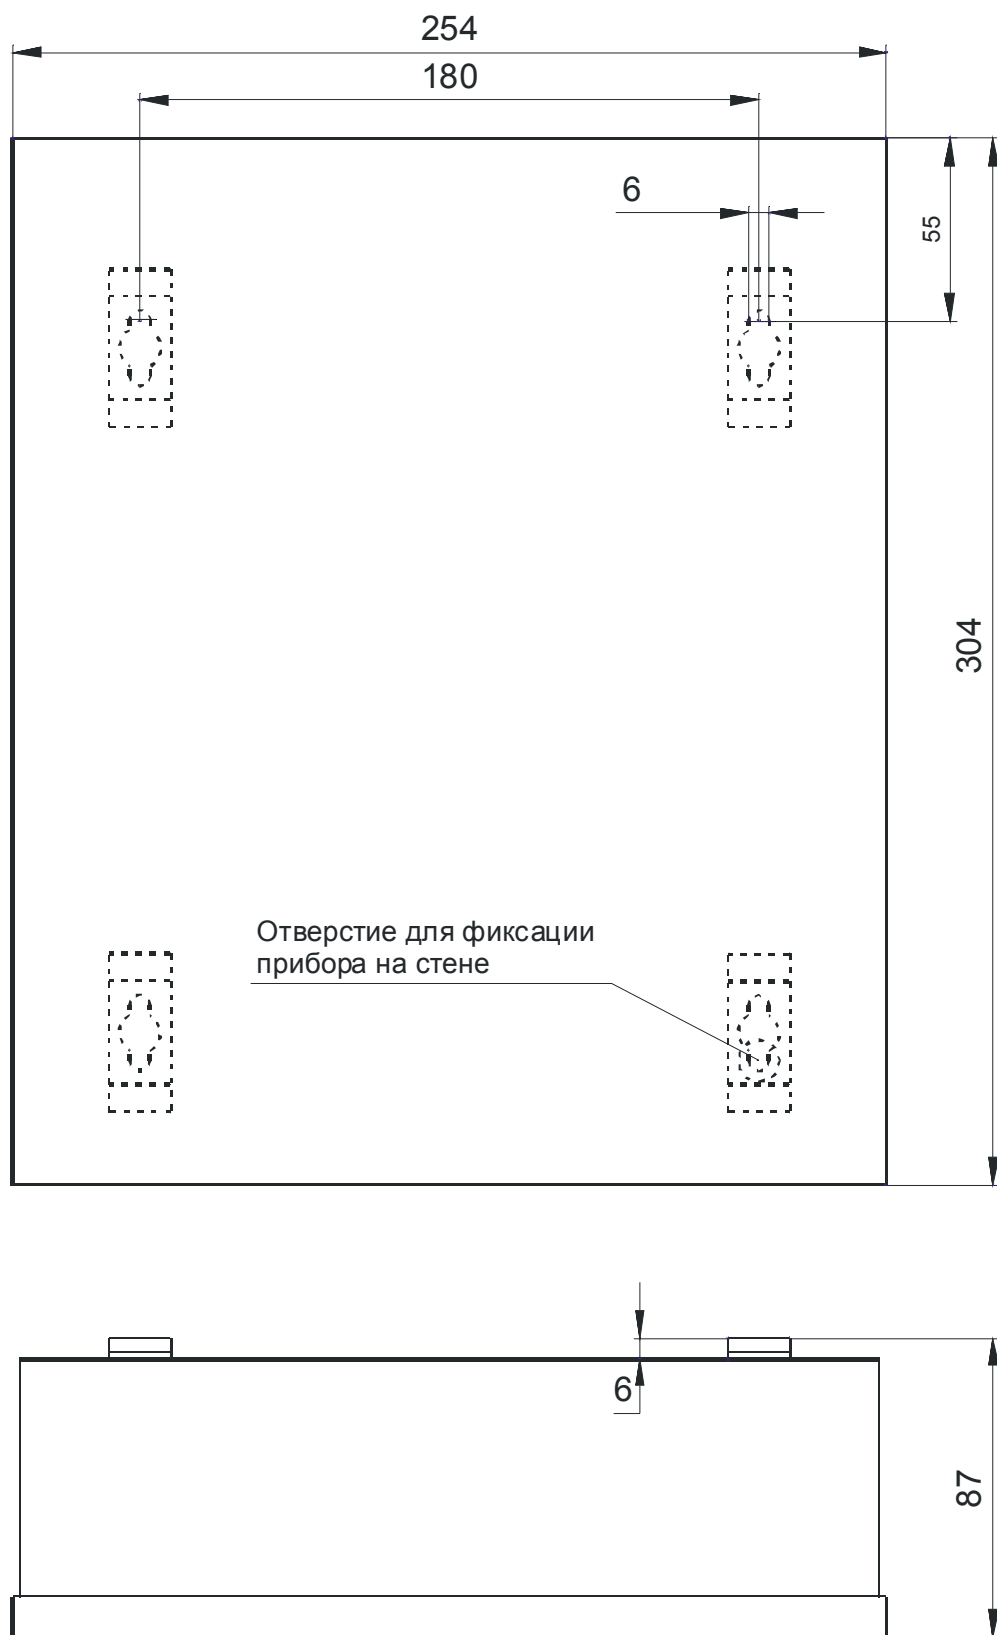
Габаритные и установочные размеры прибора «Протон-8/16»»
